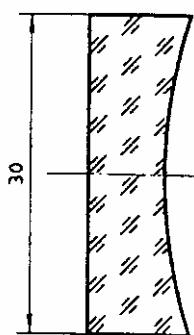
Прямоугольный цилиндрический линзовый элемент
